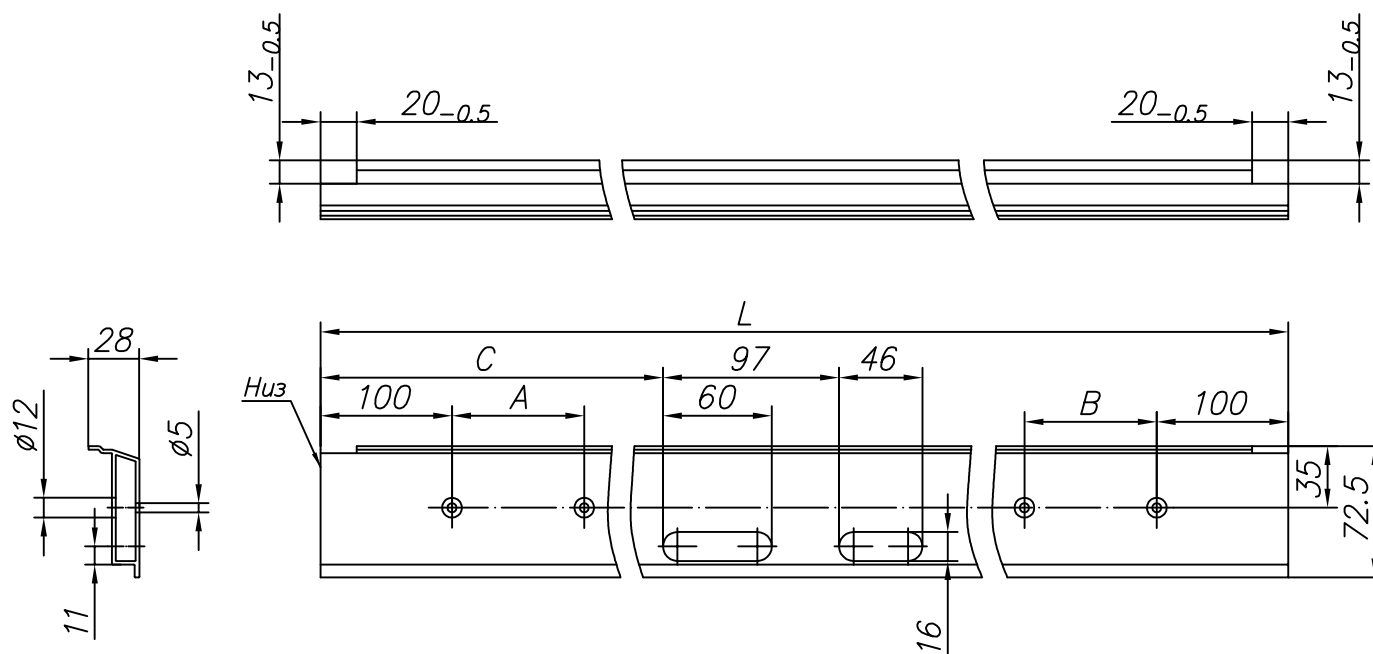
Изготовление притвора с пазом для ответной пластины замка из профиля FLGU.400.0505 (открытие внутрь, влево)
